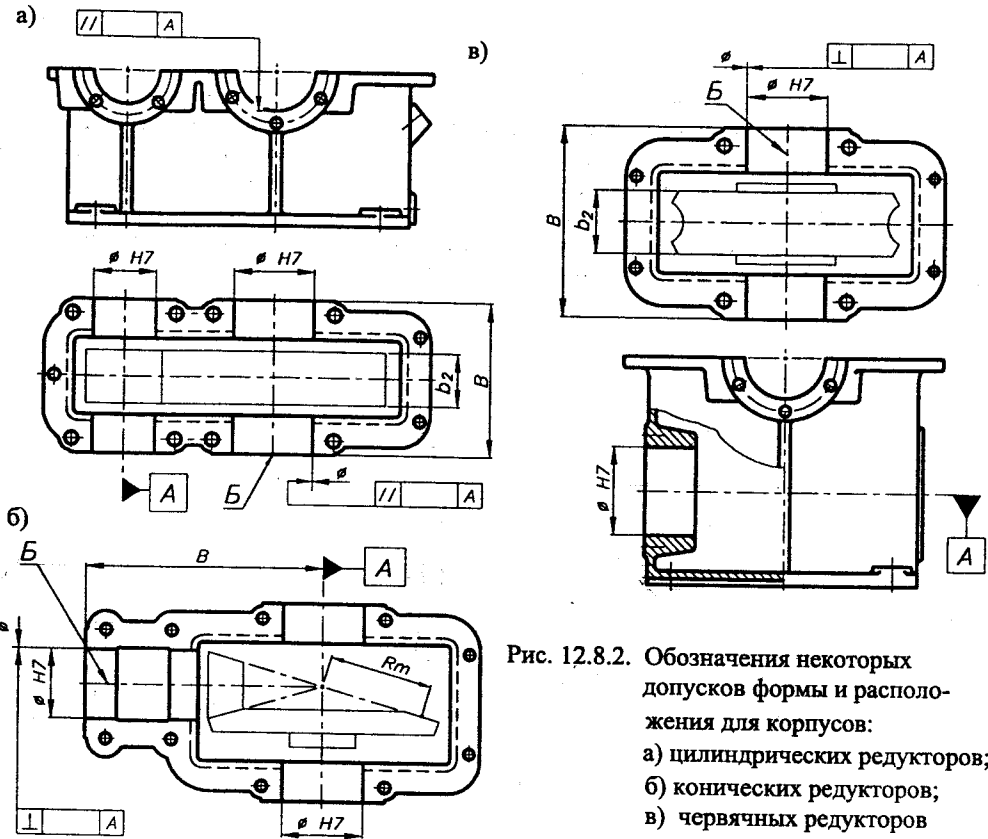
Обозначения некоторых допусков формы и расположения для корпусов: а) цилиндрических редукторов; б) конических редукторов; в) червячных редукторов
